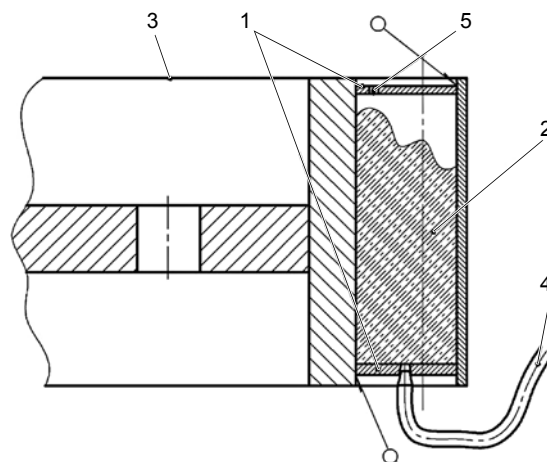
Схема заполнения полостей зубьев: 1 — приварные крышки; 2 — заполнитель (например, на основе цемента М800); 3 — сварной корпус шестерни; 4 — шланг для подачи наполнителя; 5 — сапун
